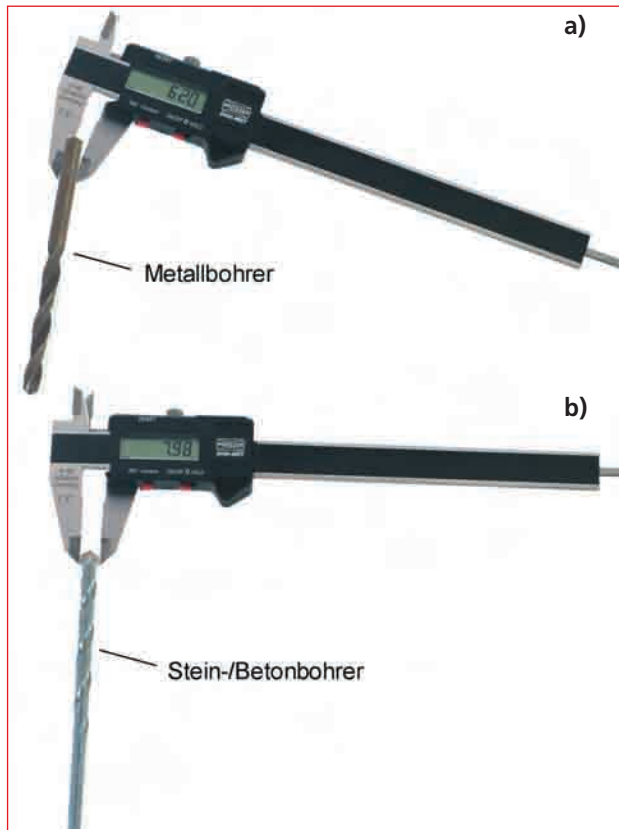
Ermittlung des Durchmessers eines Bohrers: Bei Metallbohrern wird der Durchmesser am Schaft, bei Stein- und Glasbohrern an der Klinge gemessen.
